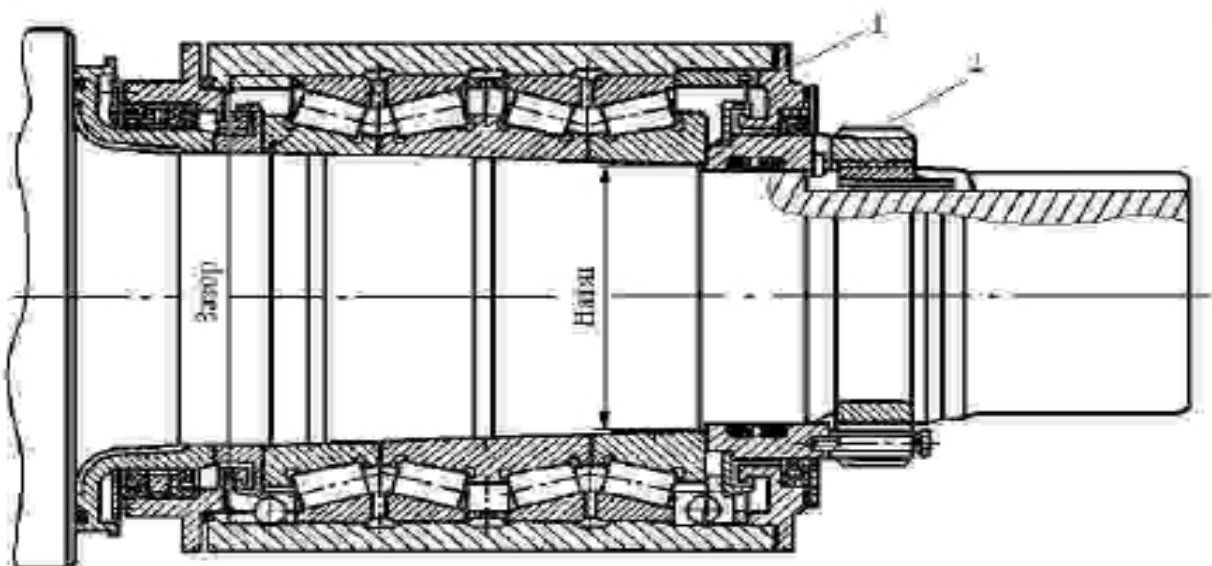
Рабочий валок листопркатного стана холодной прокатки.
